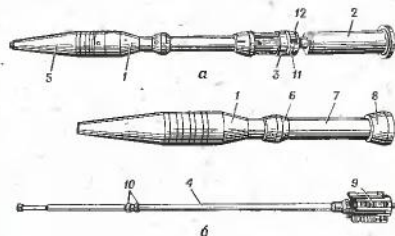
Приспособление для учебной стрельбы ПУС-9:
